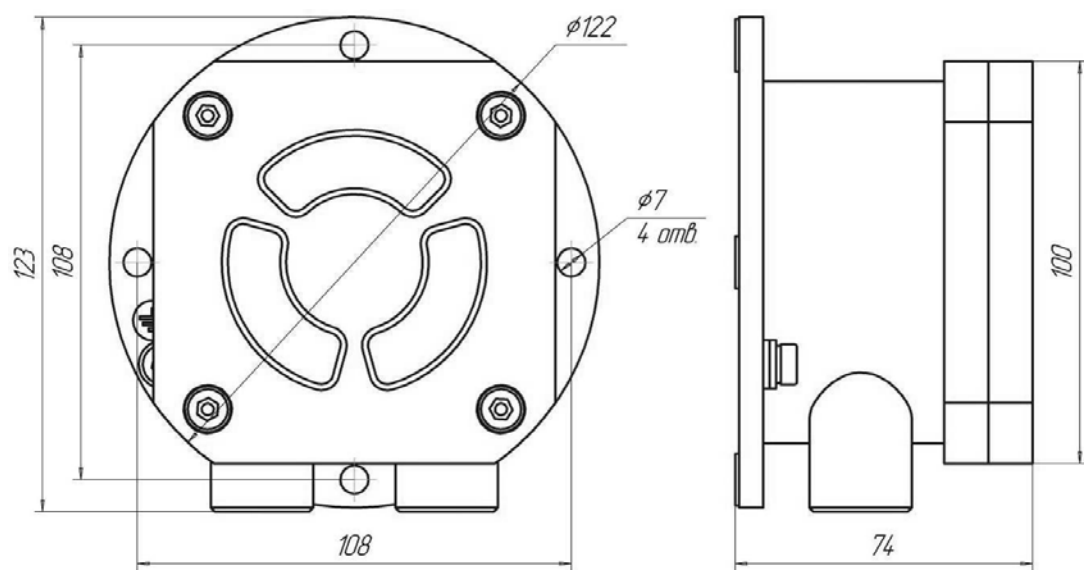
Оповещатель пожарный взрывозащищенный световой
